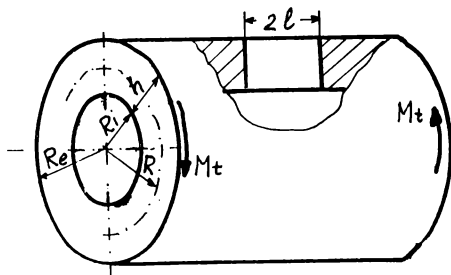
Conductă cu fisură longitudinală străpunsă sollicitată la torsiune
